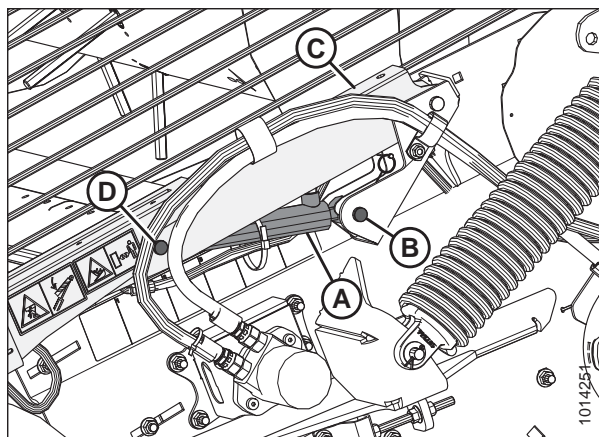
Главный гидроцилиндр — Левая сторона жатки
